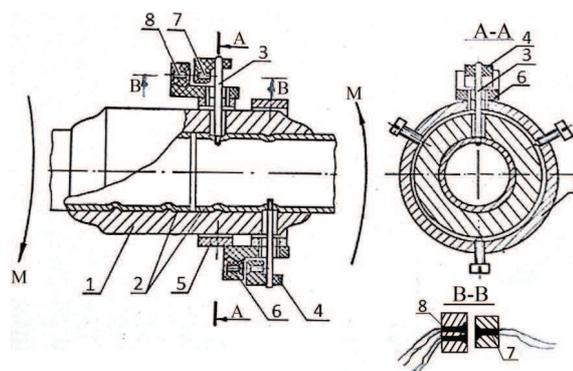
Термомеханическое соединение трубопроводов. 1 – втулка из TiNi, 2 – соединяемые трубопроводы, 3 – шток для установки кронштейна, 4 – кронштейны со светодиодами, 5 – кольцо для крепления кронштейнов, 6 – кронштейны для крепления фотодиодов, 7 – светодиод, 8 – фотодиоды
